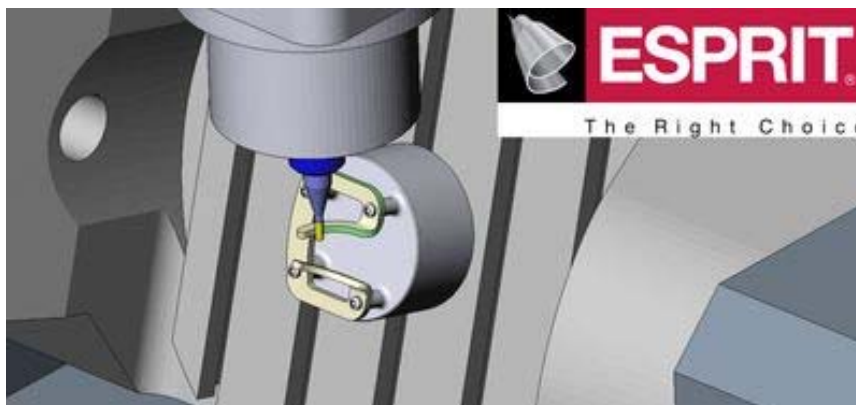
Настройка и примеры моделей адаптеров для фрезерной и токарной обработки
